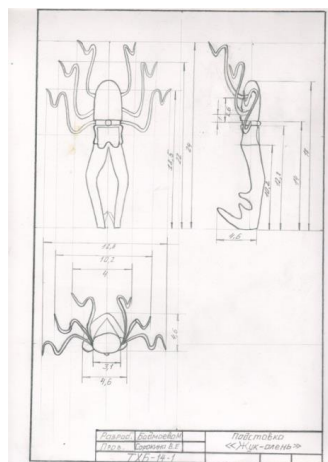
Чертеж подставки для украшений «Жук – олень»
